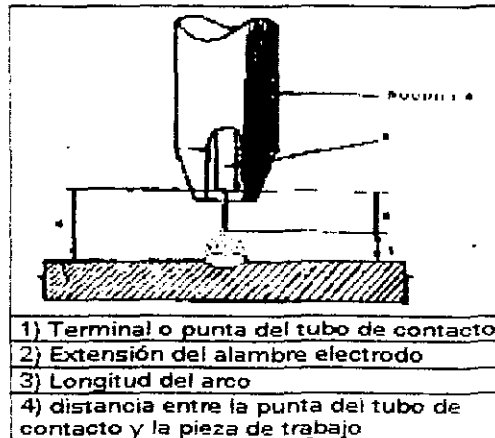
EXTENSIÓN DEL ALAMBRE ELECTRODO.
